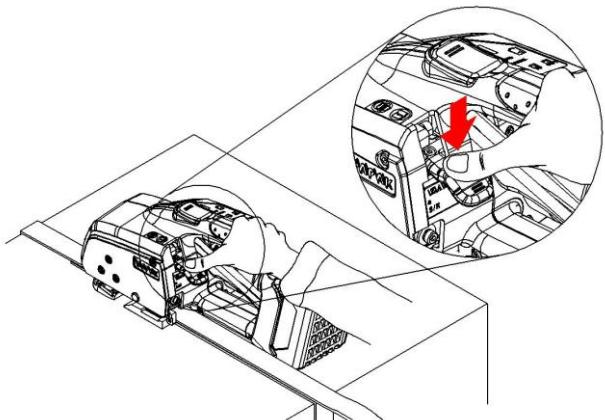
Pousser le Levier de Scellement vers le bas pour démarrer le soudage
